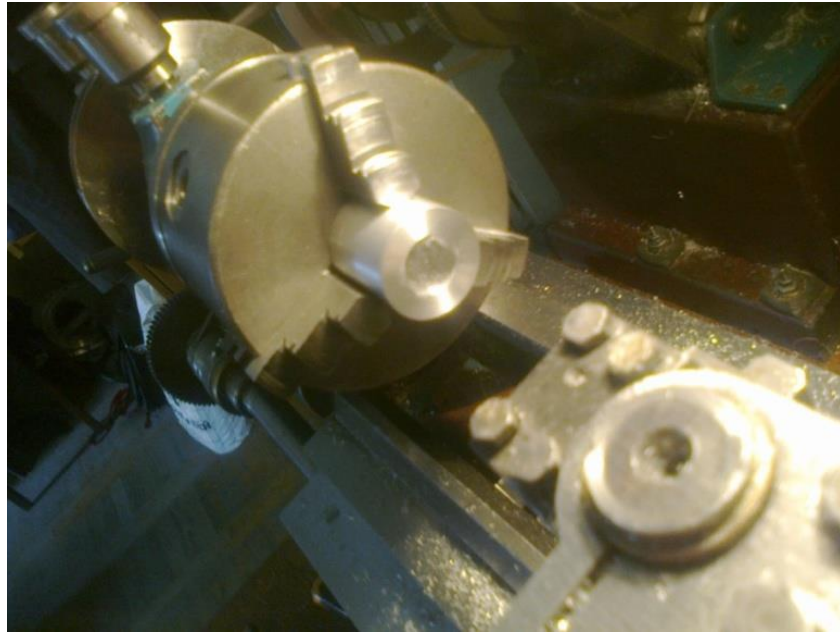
Заготовка для виготовлення рефлекторів
